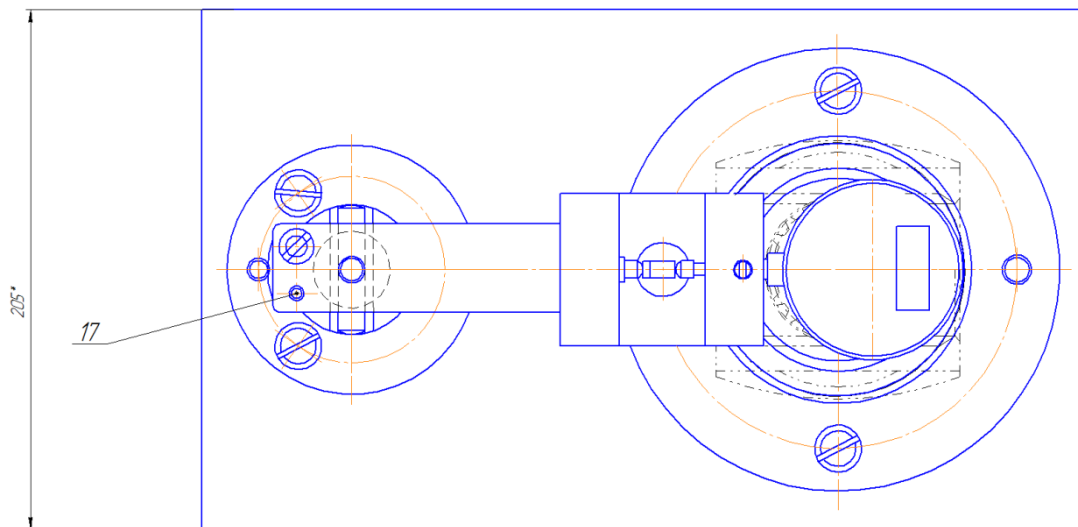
Контрольно-измерительное приспособление (вид сверху)
